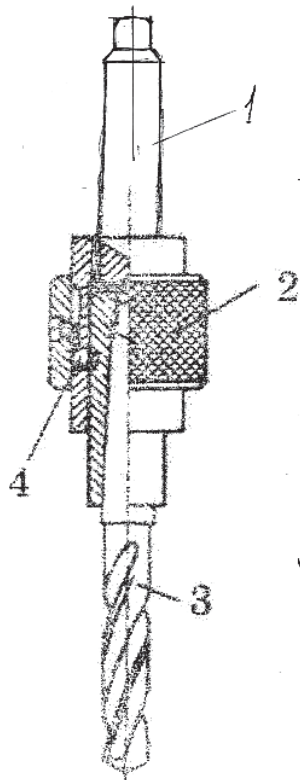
Быстросменный патрон: 1 – хвостовик; 2 – втулка; 3 – сверло; 4 – шар
